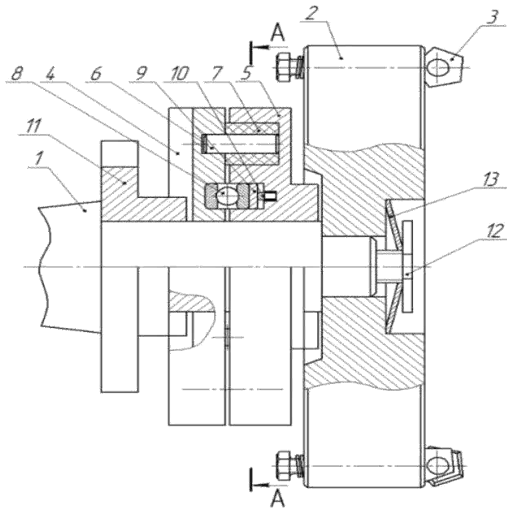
Збірна торцева фреза з демпфувальними елементами для зменшення вібрацій у процесі оброблення: 1 – оправка; 2 – торцева фреза; 3 – різальні пластини; 4 – верхнє кільце демпфувального вузла; 5 – нижнє кільце демпфувального вузла; 6 – сталеві кульки; 7 – демпфувальний елемент; 8 – повідець; 9 – гвинт; 10 – пружна шайба [16]
